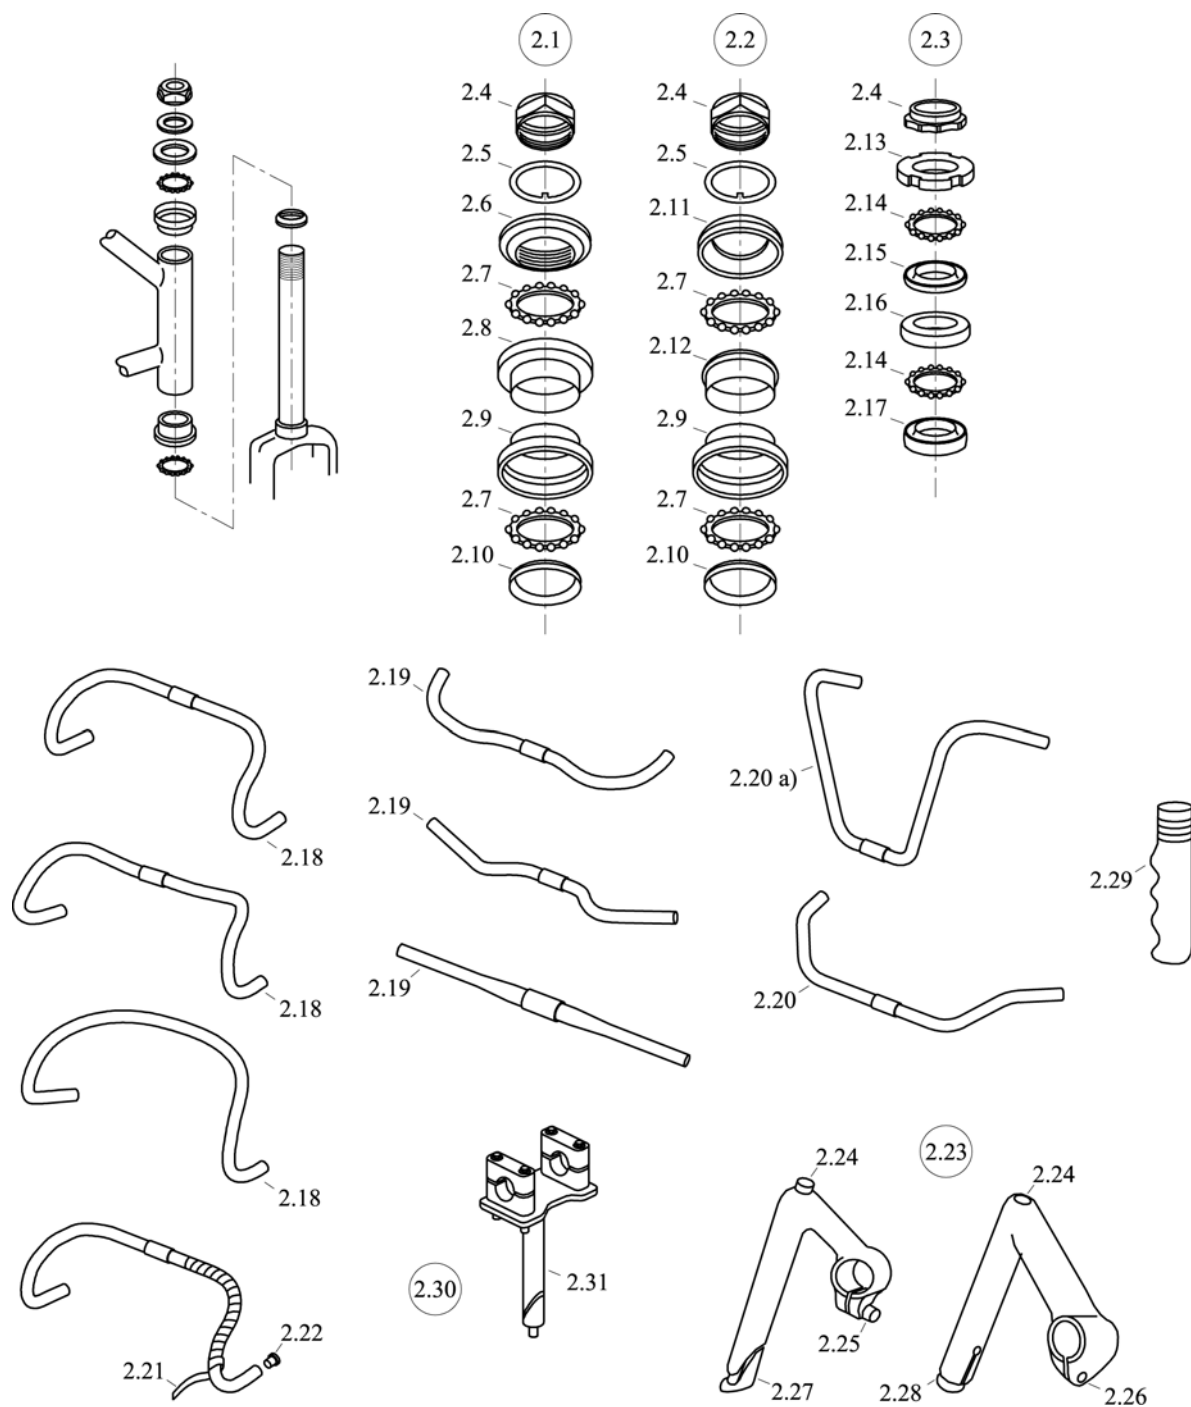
Ensemble de Direction / Head Assembly / Steuersatz und Lenkung / Gruppo sterzo / Balhoofd samenschooling
